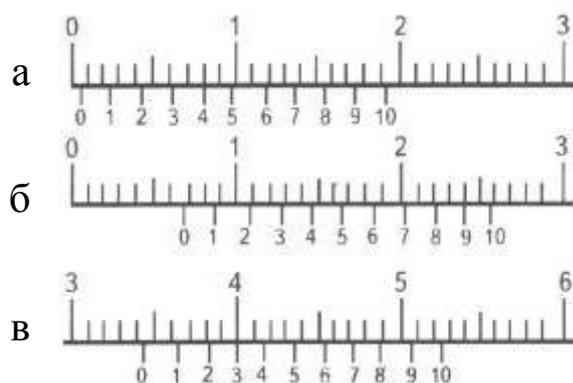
Примеры измерения штангенциркулем. Положение шкалы штанги и нониуса при измерении размеров: а – 0,4 мм; б – 6,9 мм; в – 34,3
